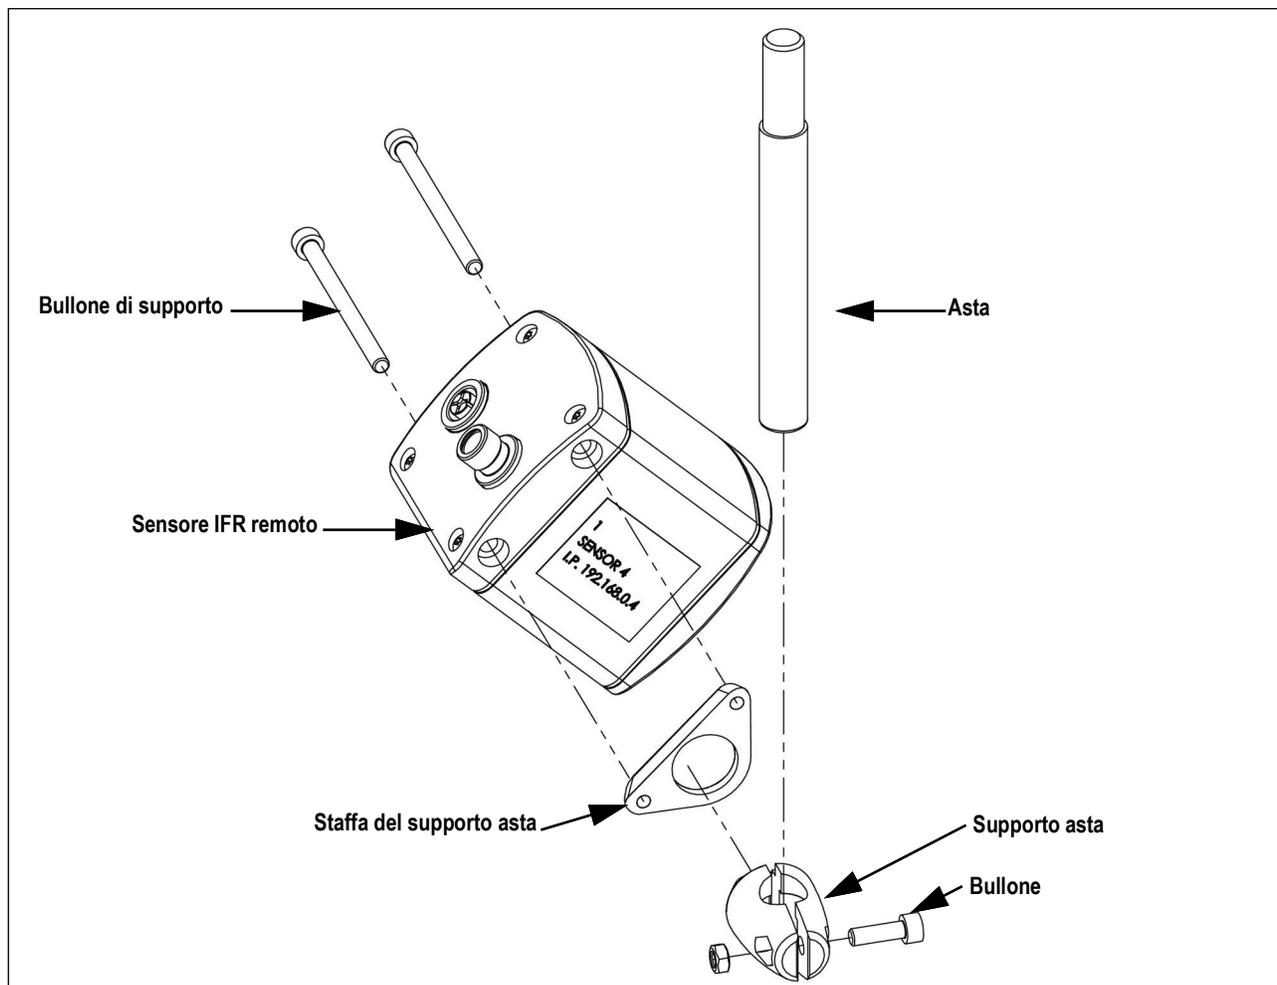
Assemblaggio del gruppo sensori IFM remoti
